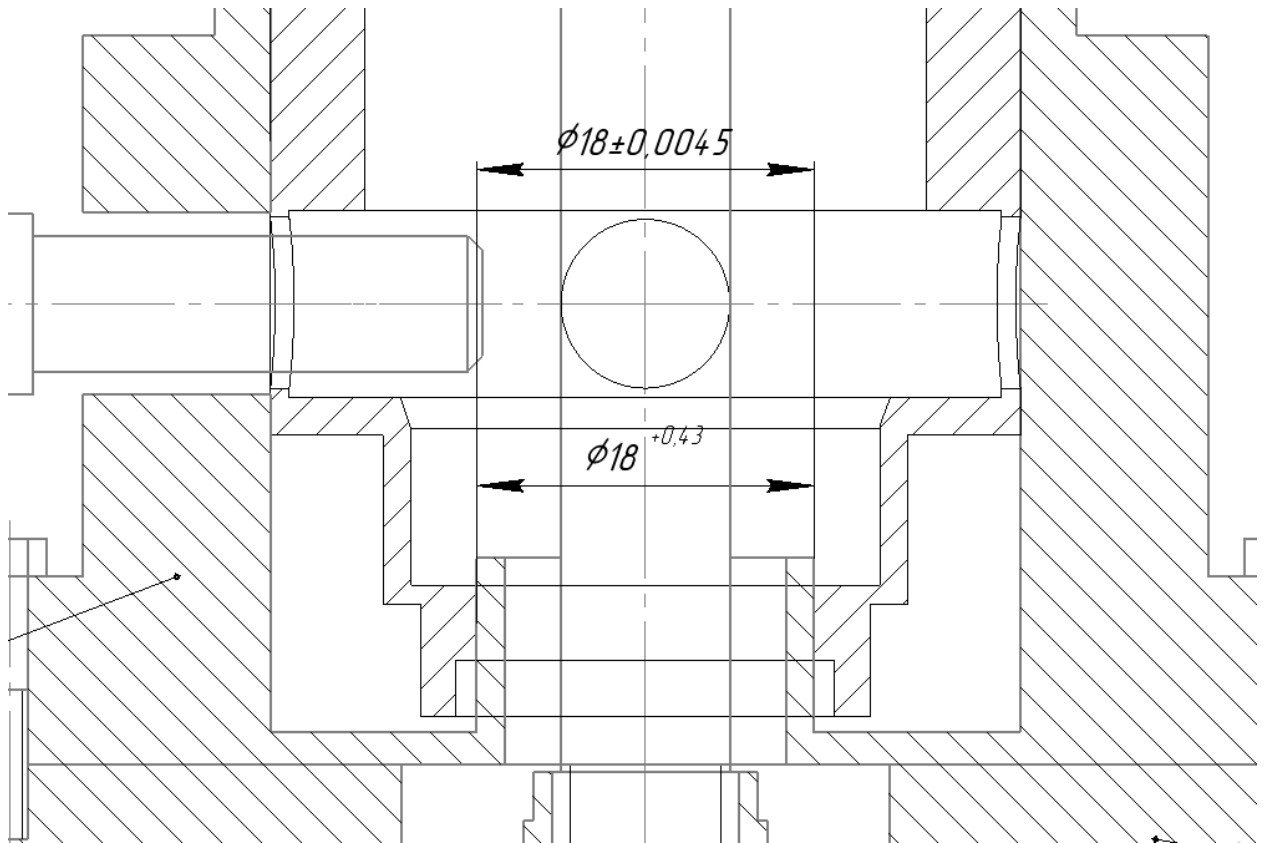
Ескіз для визначення зазору між внутрішньою поверхнею деталі та установчим стаканом
